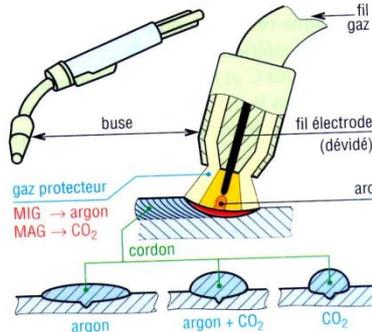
Principe des soudages MIG et MAG. [8]
